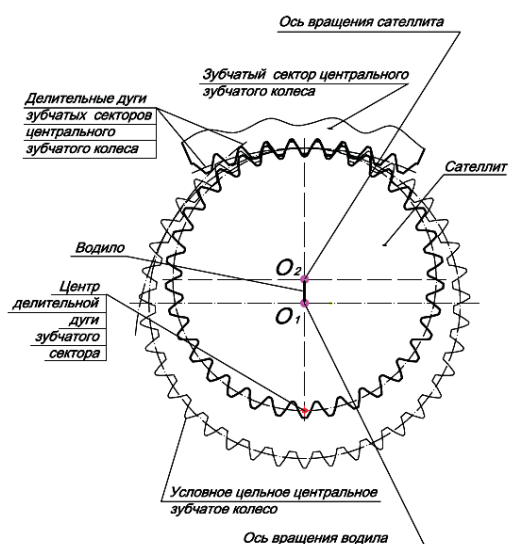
Зацепление сателлита и сектора центрального зубчатого колеса планетарной плавнорегулируемой передачи
